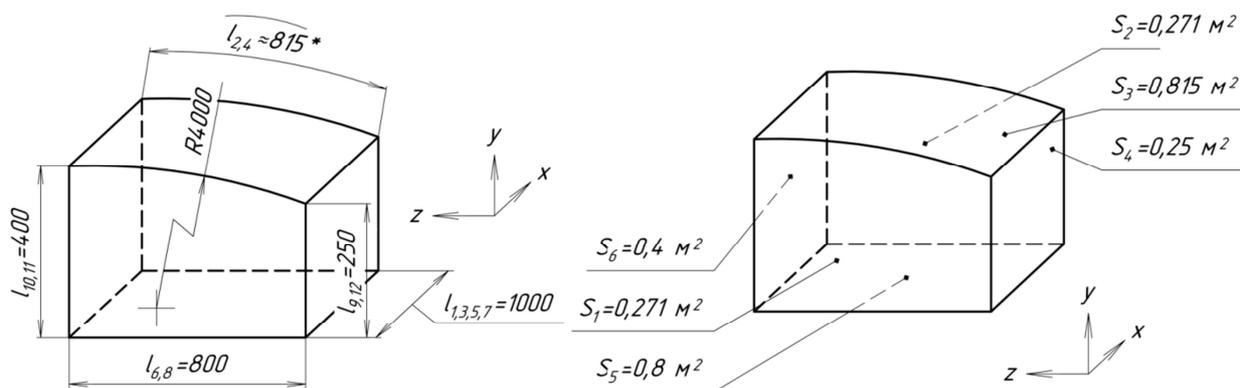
Схема расположения и обозначения элементов каркаса и панелей сварного отсека
